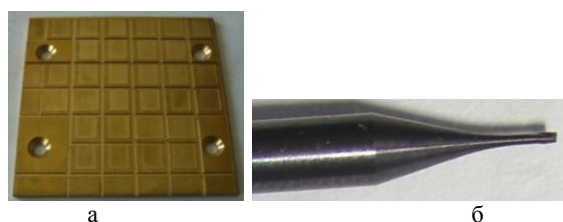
Заготовка з ділянками обробки мікрофрезеруванням та фреза діаметром 0,5 мм, яка використана в процесі обробки: а – заготовка, б – інструмент
